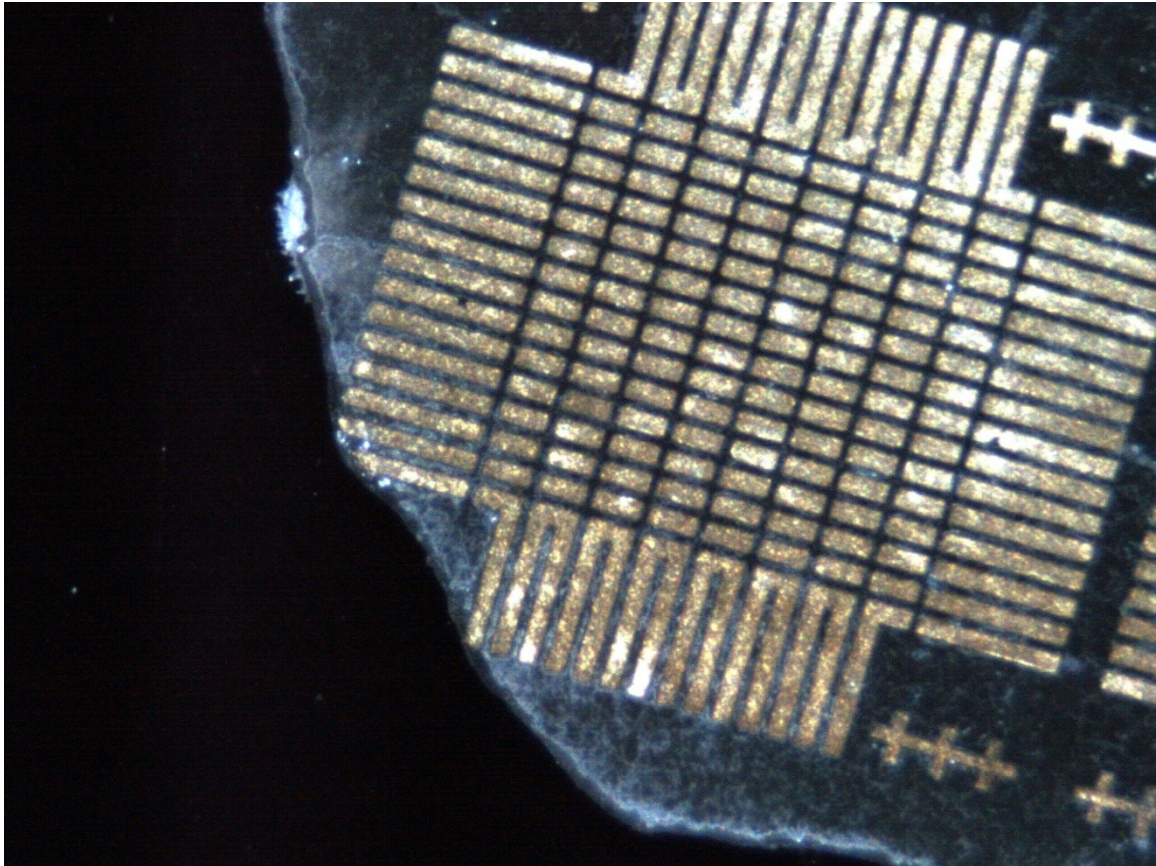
Échantillon pour test de mouillage de la pâte de soudure avec la brasure d'or de l'Université de Melbourne
